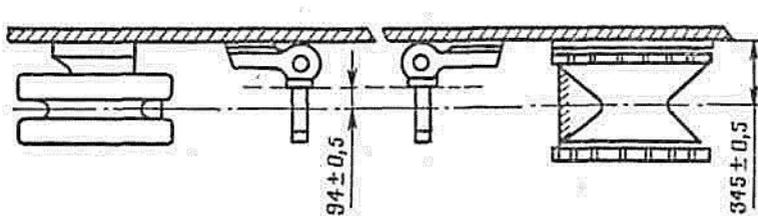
Схема проверки положения балансиров при установке колеи танка
